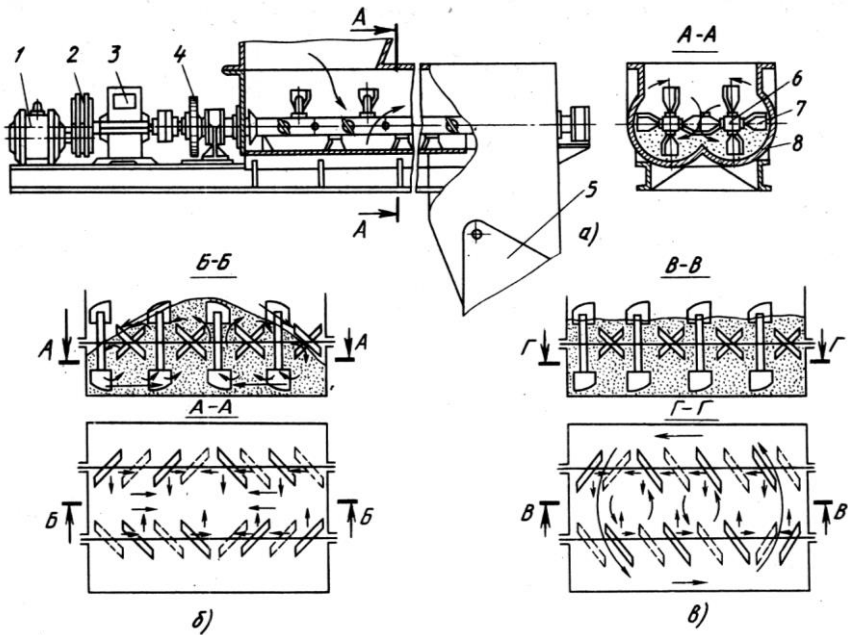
Устройство и схемы движения материала двухвального смесителя:
